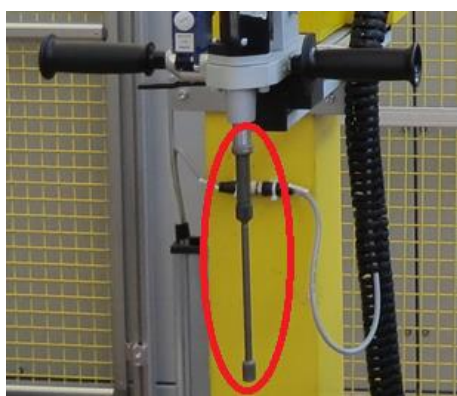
Гайковерт для затяжки болтов крепления масляного картера
